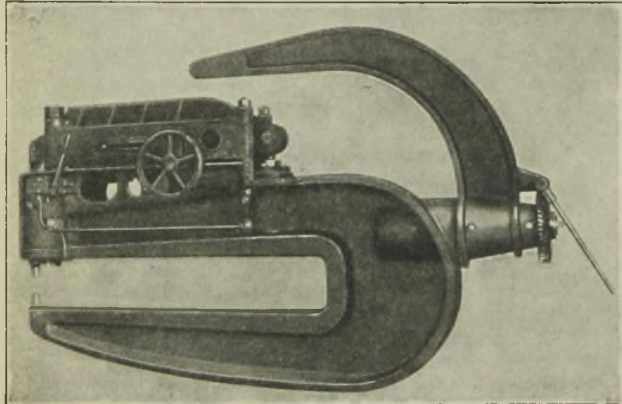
Wasserdruck-Nietmaschine mit einstellbarem Schließdruck.
